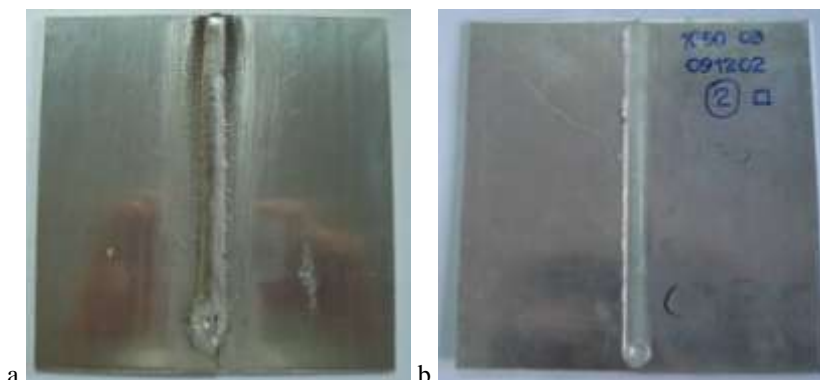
Probetas soldadas: a- GMAW y b- FSW.
